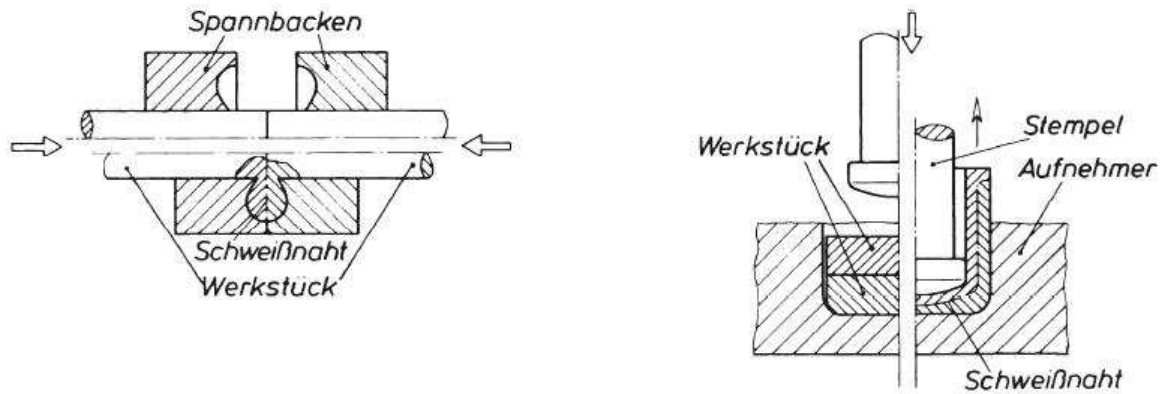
Anstauchschweißen (links) und Fließpressschweißen (rechts)<sup>[ST02]</sup>
